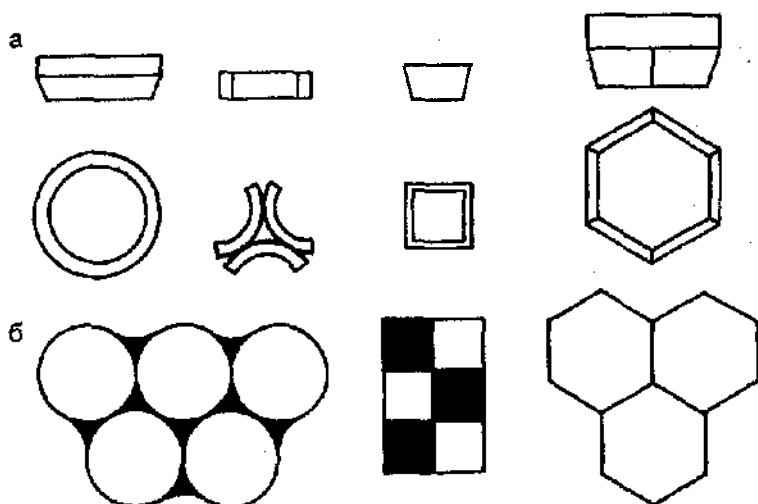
Матрицы для торцевой мозаики (а) и внешний вид мозаики (б)
